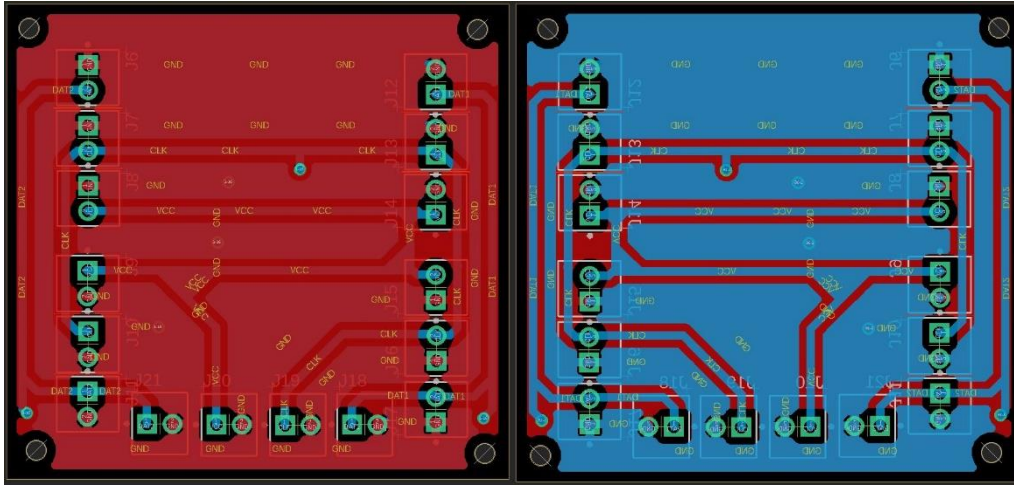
(a)Diseño PCB intermedia cara TOP(izquierda). Fig.32 (b) Diseño PCB intermedia cara BOTTOM(derecha).
